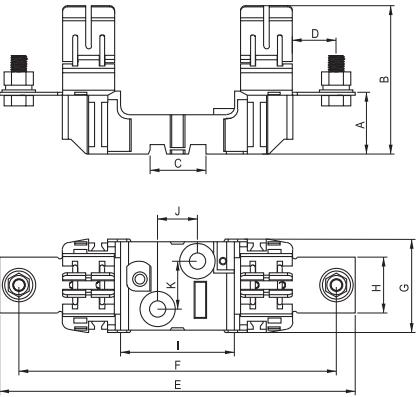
Габаритные размеры плавкой вставки / Figure 1 – Overall dimensions of a fuse-link
